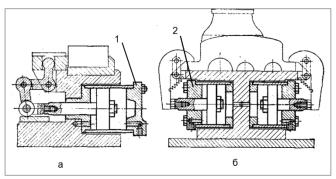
Примеры применения в станочных приспособлениях встраиваемых пневмоцилиндров с крышкой: а – задней; б – передней
